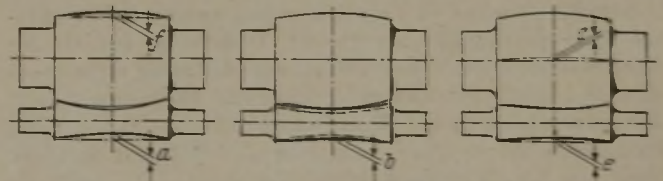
Walzendurchbiegung und -ausdehnung für Vierwalzengerüste.
